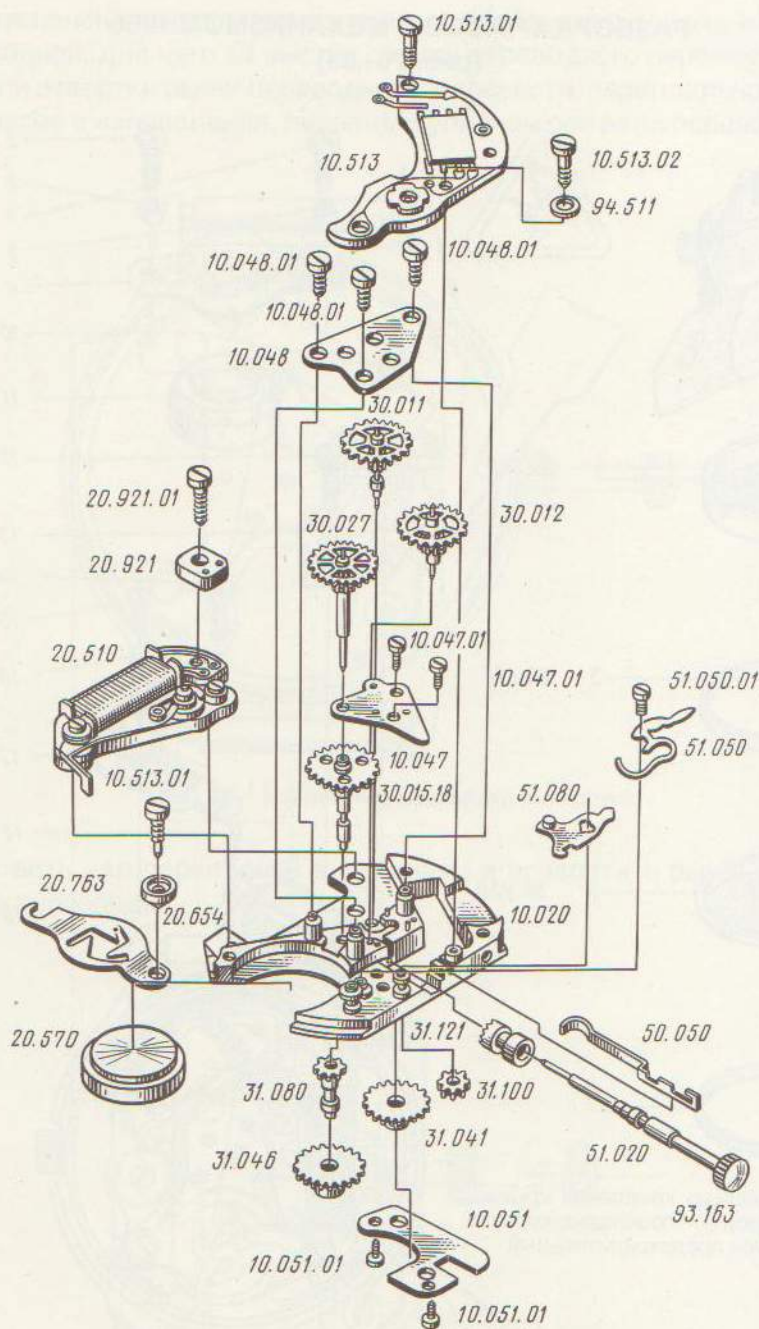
Детали и сборочные единицы механизма часов 1956:
